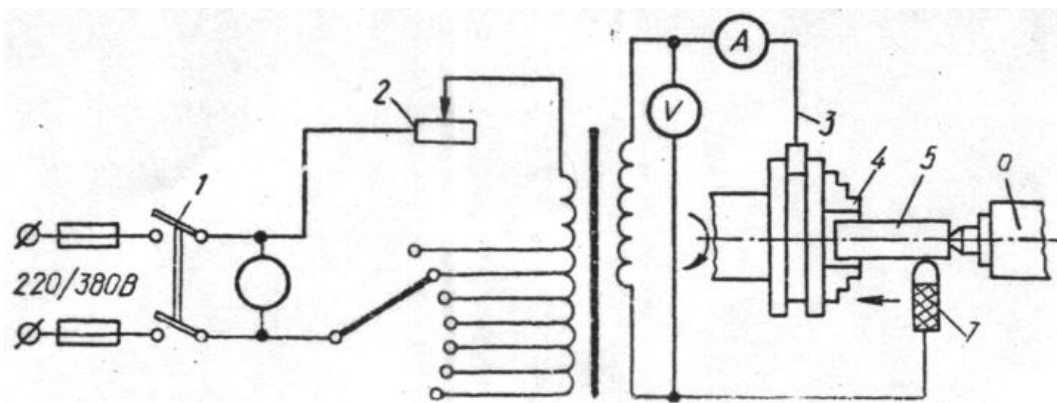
Принципіальна схема установки для електромеханічної обробки:
